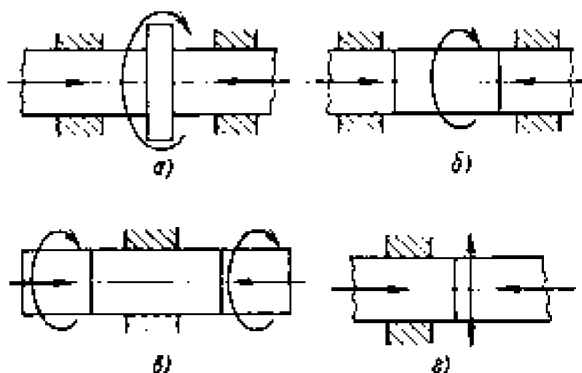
Разновидности процесса сварки трением:
